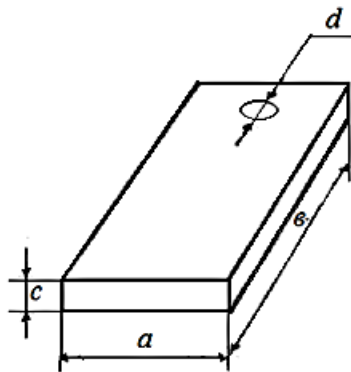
Экспериментальный образец из стали 40Х: a – ширина, b – длина, c – толщина, d – диаметр отверстия
